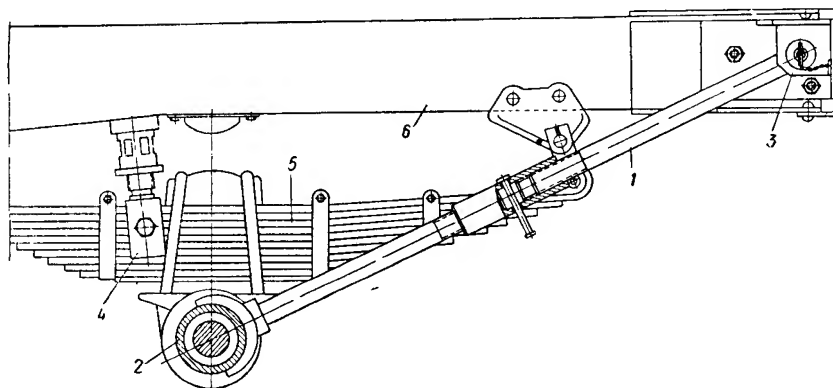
Приспособление для разгрузки рамы; 1 — штанга; 2 — кожух полуоси автомобиля; 3 — кронштейн; 4 — приспособление для разгрузки рессор; 5 — рессора; 6 — рама автомобиля.
